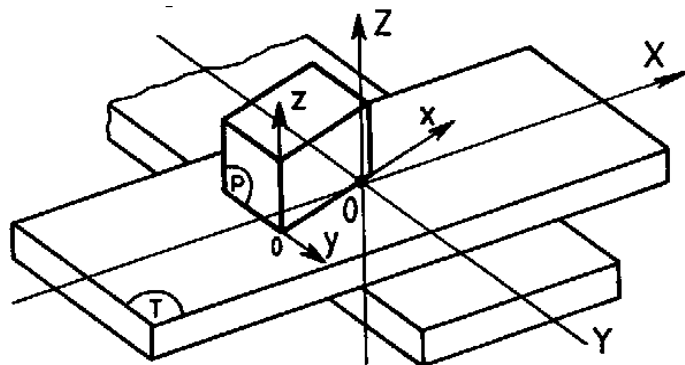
a) Référentiel de la pièce par rapport R machine-outil
